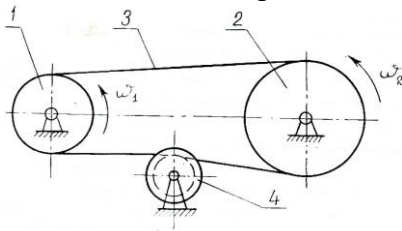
Кинематическая схема ленточного транспортера с натяжным роликом
